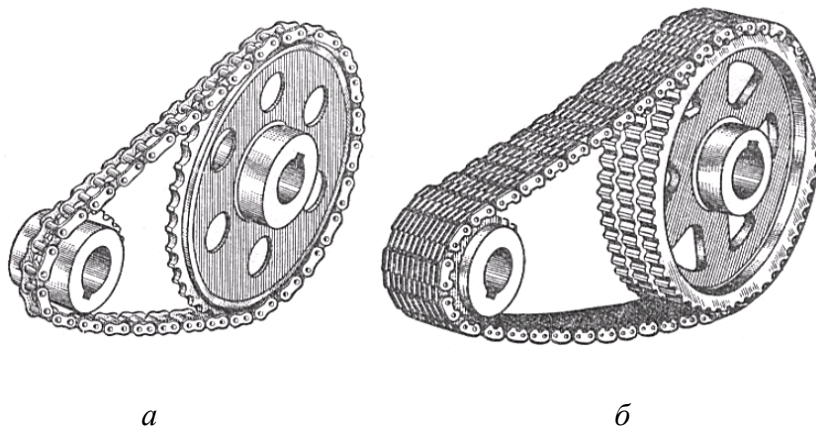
Цепная передача: а – роликовой цепью; б – зубчатой цепью
